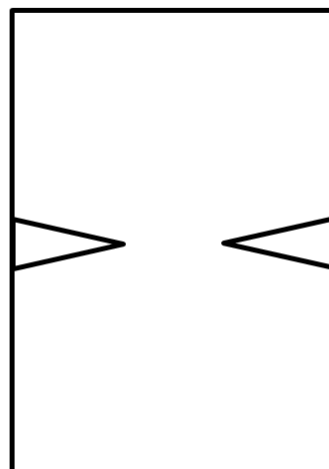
Kerbwerkzeug um einen definierten Querschnitt in die Zugprüfkörper einzuschneiden.
